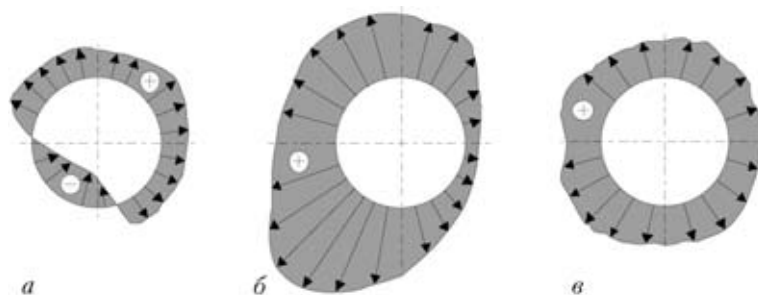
Эпюры распределения магнитного поля H_p вдоль кольцевого сварного соединения контактной сварки клапана с поршнем: а — недогрев металла; б — перегрев; в — оптимальное качество сварки
